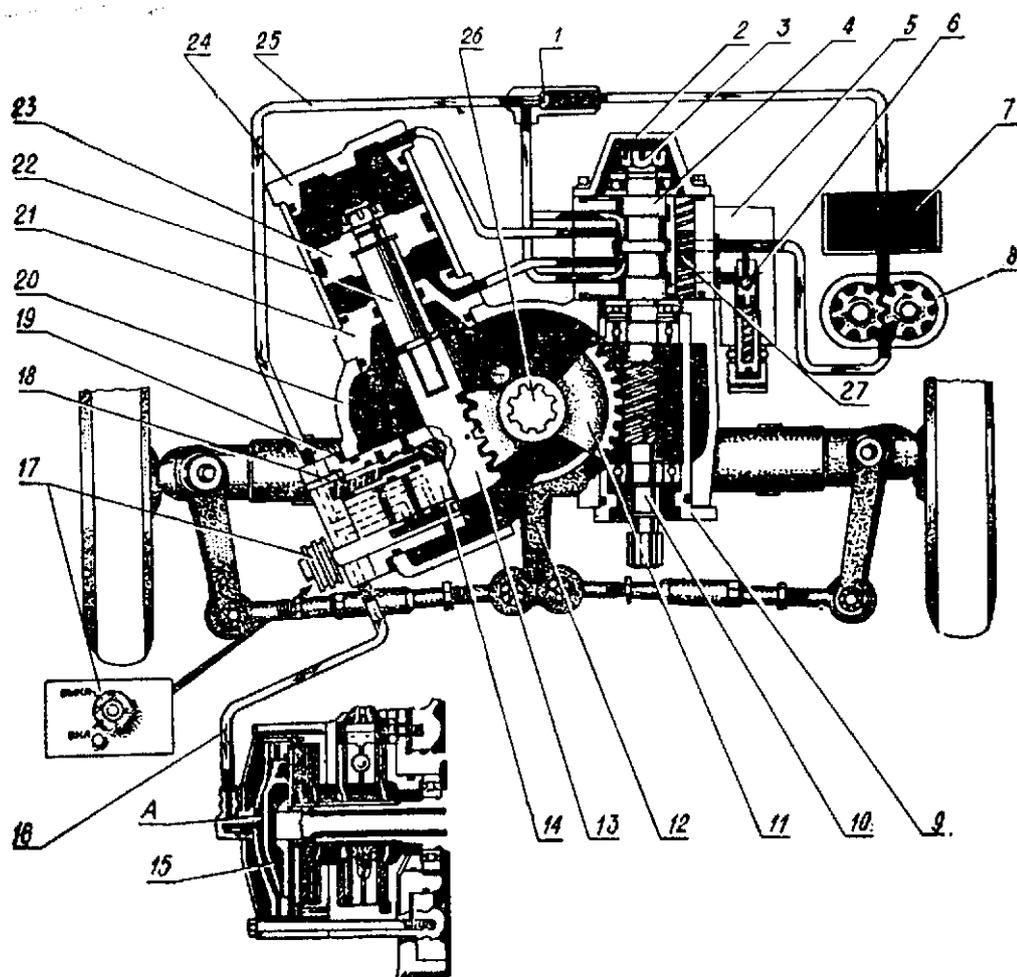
Схема гидроусилителя рулевого управления и блокировки дифференциала:
